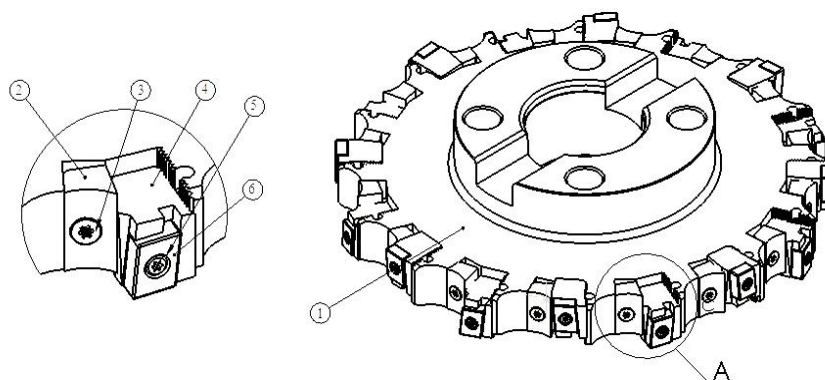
Конструкция сборной дисковой трехсторонней фрезы фирмы Pramet
